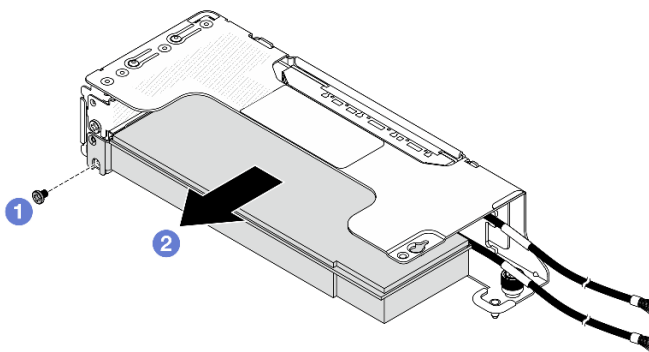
Entfernen eines PCIe-Adapters aus dem 2LP-Adapterrahmen
